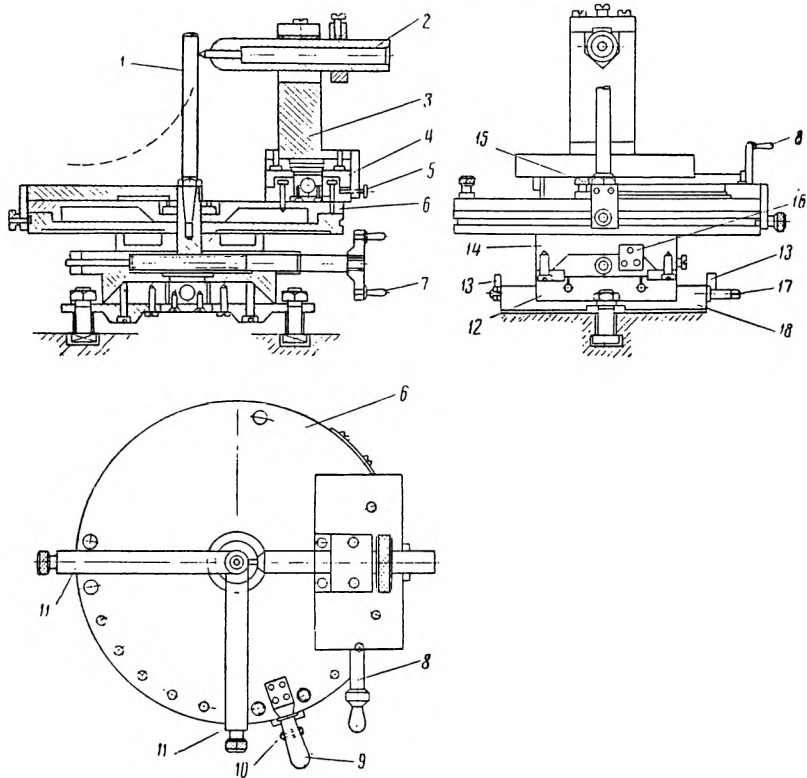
Универсальное приспособление конструкции Андрианова и Шестова для профилирования шлифовального круга
